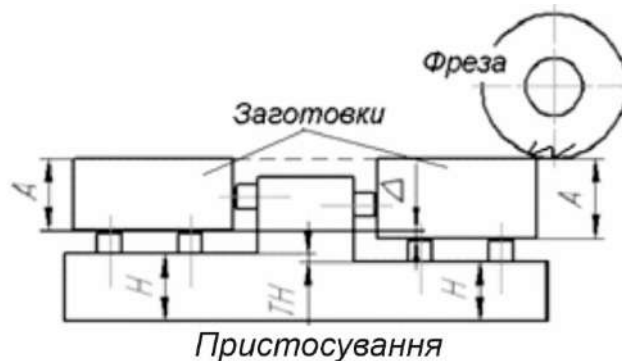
Встановлення деталі у багатомісний пристрій
